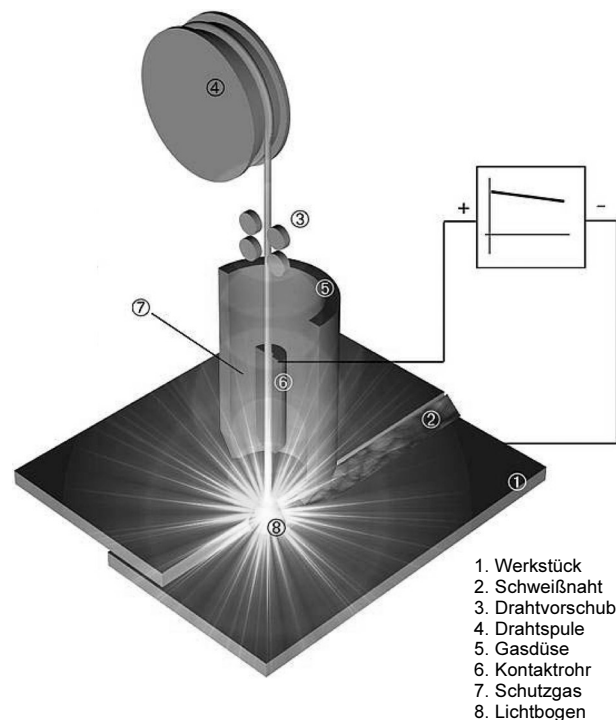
Schematische Darstellung MIG-Schweißen.
